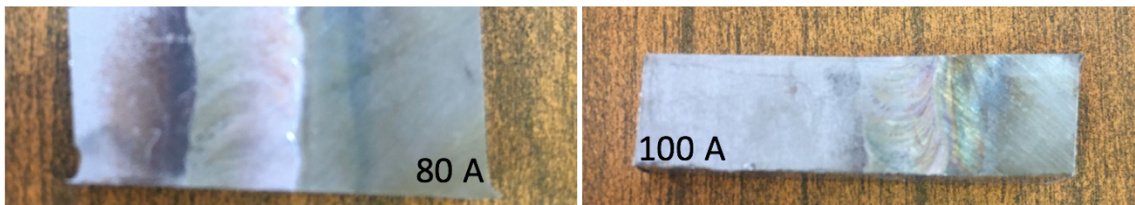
Cordones de soldadura, probeta empleada en el ensayo de micro y macro estructura, dureza Vickers y HRB.
